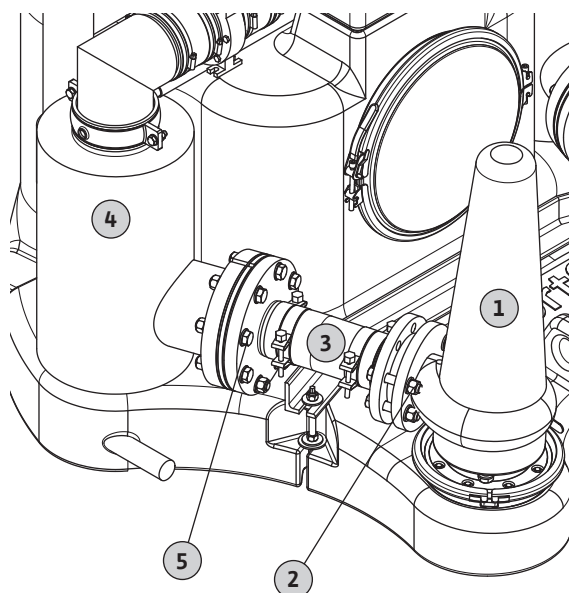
Очистка резервуаров для сбора твердых отходов
